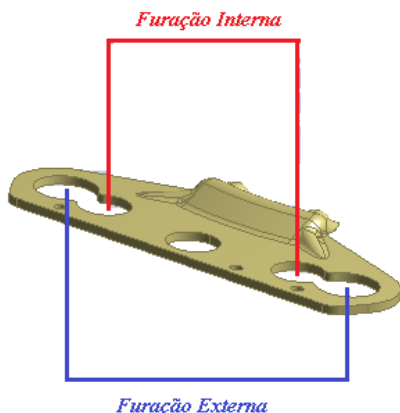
Placa base soldada ao bloco de aço.
